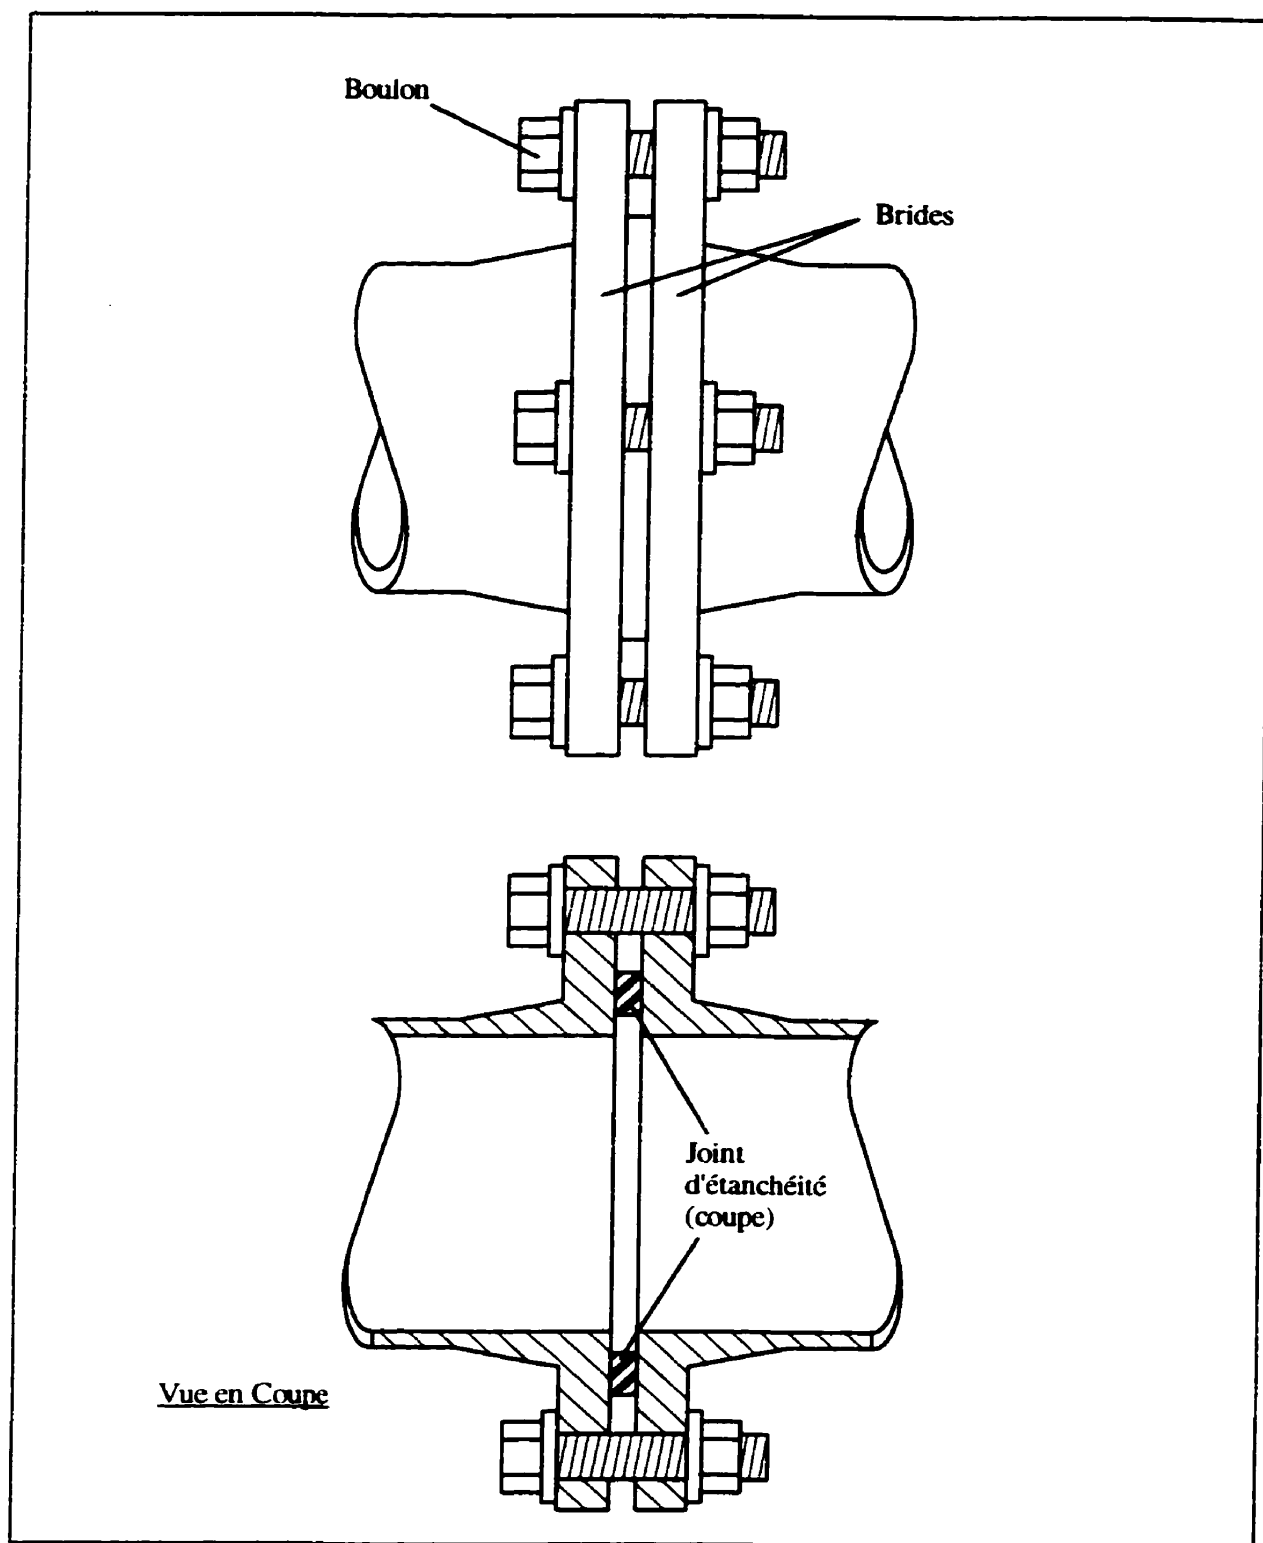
Exemple de raccord avec joint d'étanchéité entre deux conduites
